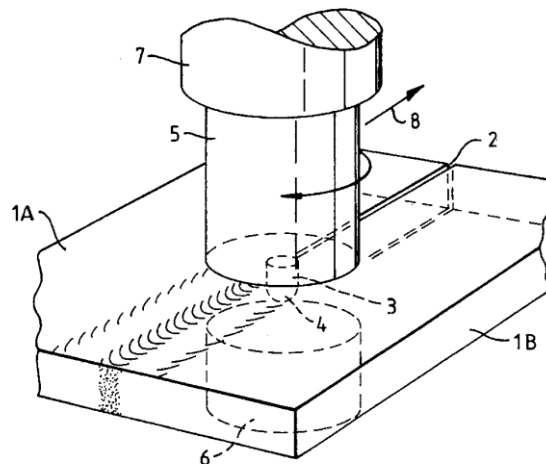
Aufbau des Rührreibschweißverfahrens [39]
